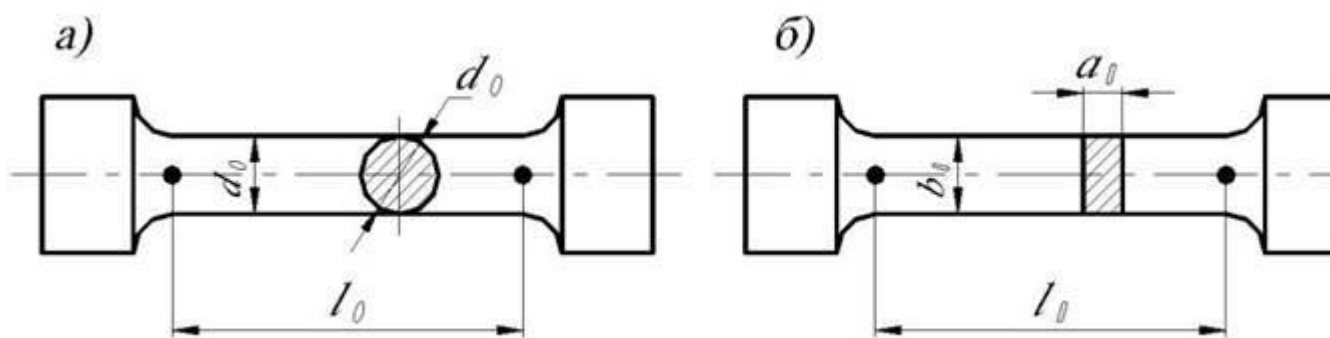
образцы для испытаний на разрыв: а – круглый; б – плоский
